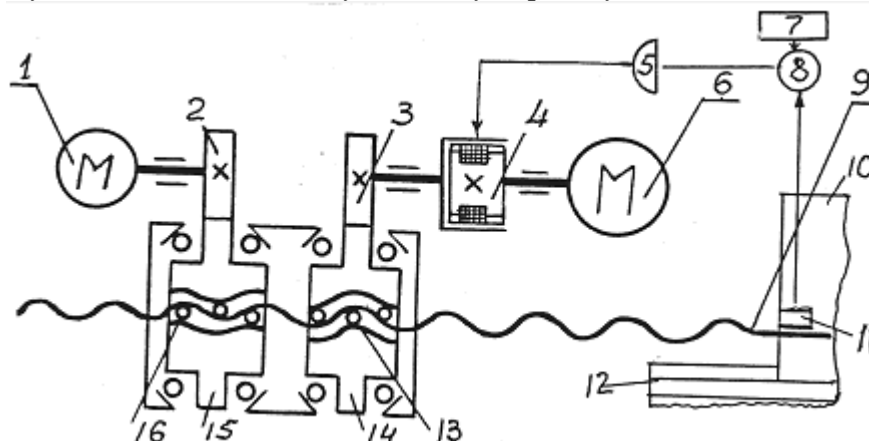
Схема приводу зворотно-поступального руху подачі
